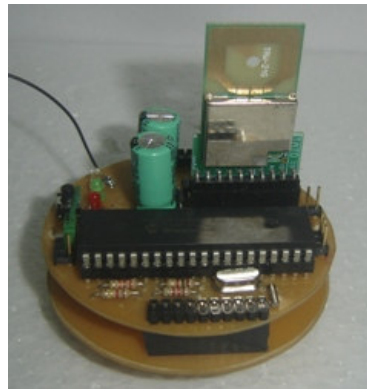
Placas do módulo remoto montadas e conectadas.
